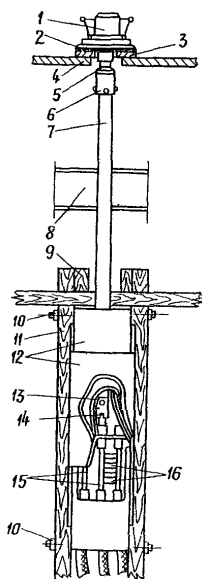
Монтаж привода переключателя барабанного типа 1 - колпак привода; 2 - крышка сальника; 3 - фланец, приваренный к крышке бака; 4 - крышка бака; 5 - вал привода; 6 - верхняя муфта штанги; 7 - штанга привода; 8 - ярмовая балка; 9 - горизонтальная деревянная планка, скрепленная с ярмовой балкой 8 и стойкой 11; 10 - шпильки из изоляционного материала; 11 - вертикальная деревянная стойка; 12 - бумажно-бакелитовые цилиндры; 13 - нижняя муфта штанги; 14 - втулка переключателя; 15 - контактные трубы; 16 - контактные кольца
